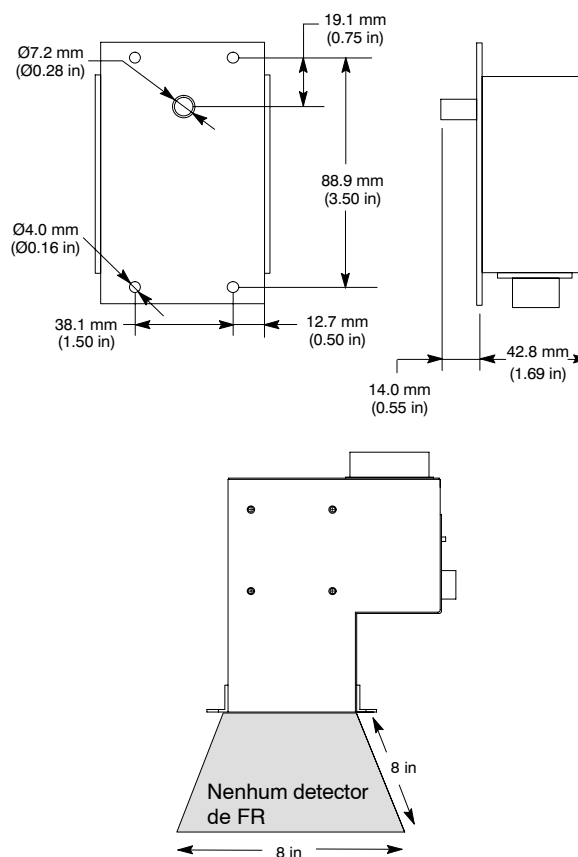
Dimensões do detector de FR e instruções de montagem
